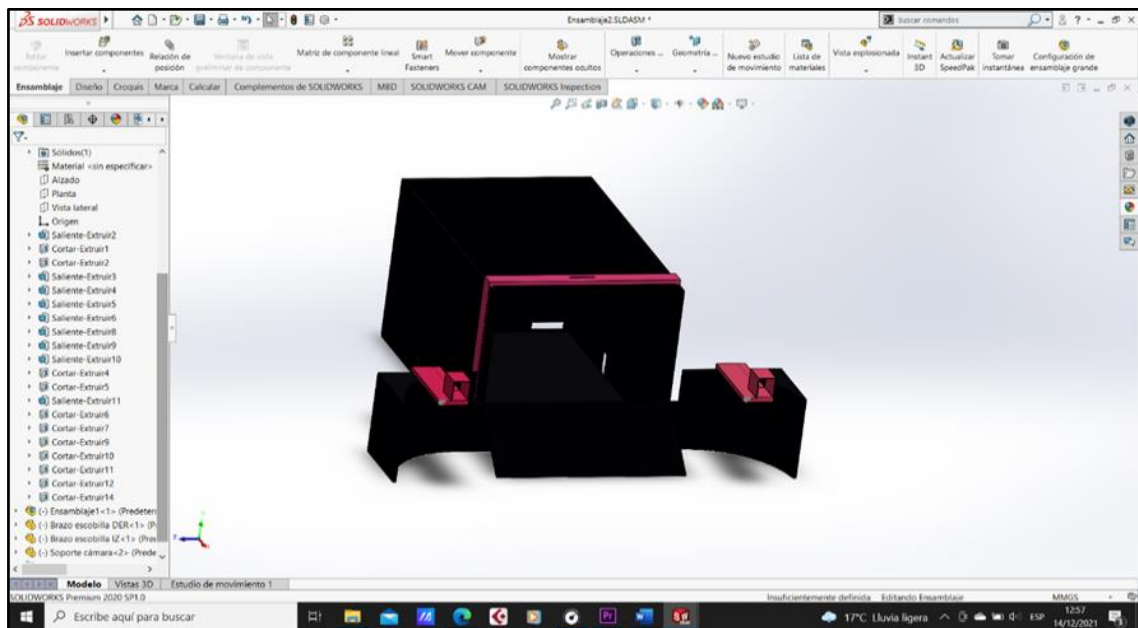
Ensamblaje de las piezas del chasis del prototipo
